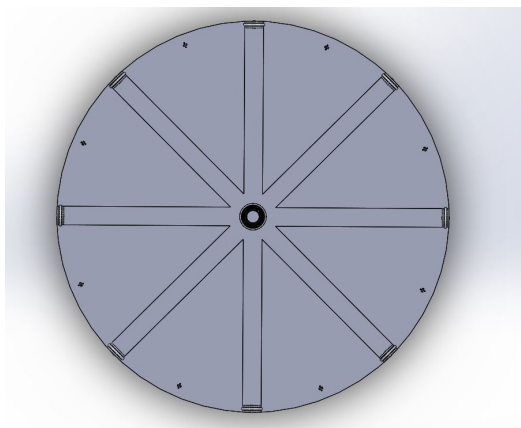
Vista frontal de base inferior, rodamiento cónico y ruedas de soporte
